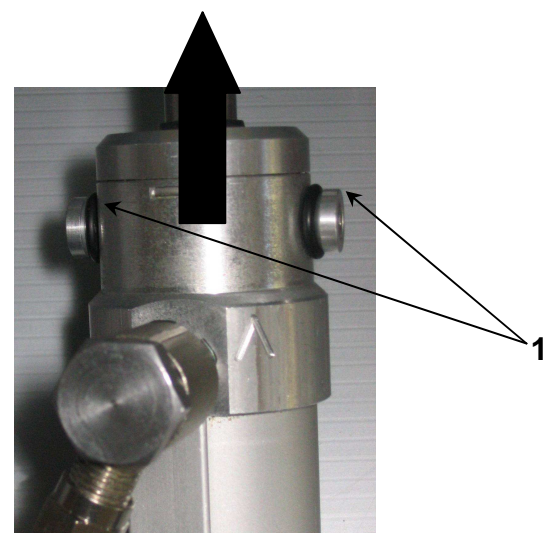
Sposób montażu elastycznych przewodów instalacji pneumatycznej
